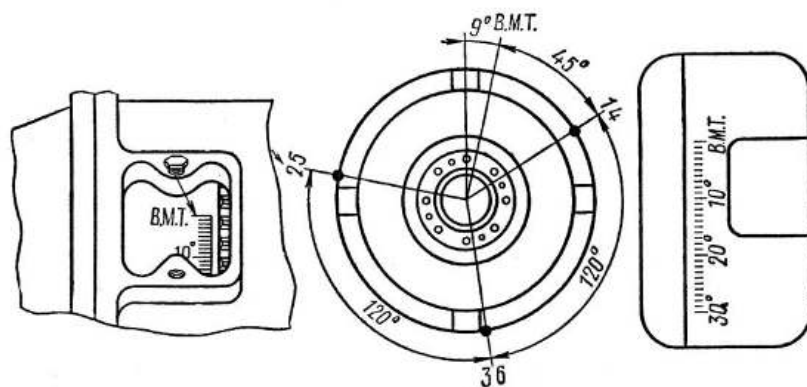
Вид на указатели и метки при регулировке клапанного механизма двигателя СМД-62
